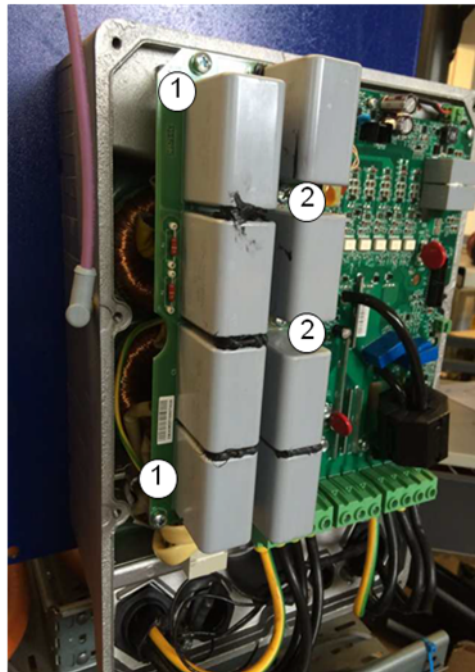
Befestigung des werkseitigen eingebauten Kondensatormodul
